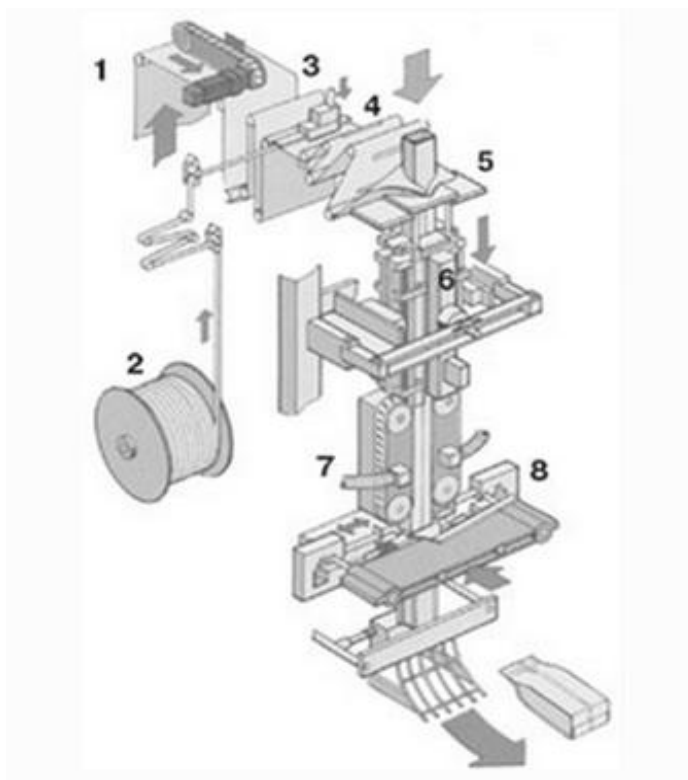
Принцип роботи вертикальної шлангової машини ROBERT BOSCH періодичної дії з натягуванням вакуумних ременів, зварюванням країв і вставкою ZIP-застібки (GMBH): 1 - подача пакувального матеріалу; 2 - рулон з ZIP-застібкою; 3 - зварювальний вузол (склеюючий) ZIP-кріплення; 4 - зварювання (склеювання) ZIP-застібки; 5 - формуючий комір; 6 - поздовжня термоущільнювальна накладка; 7 - вакуумні всмоктувальні ремені; 8 - поперечні блоки ущільнення.
